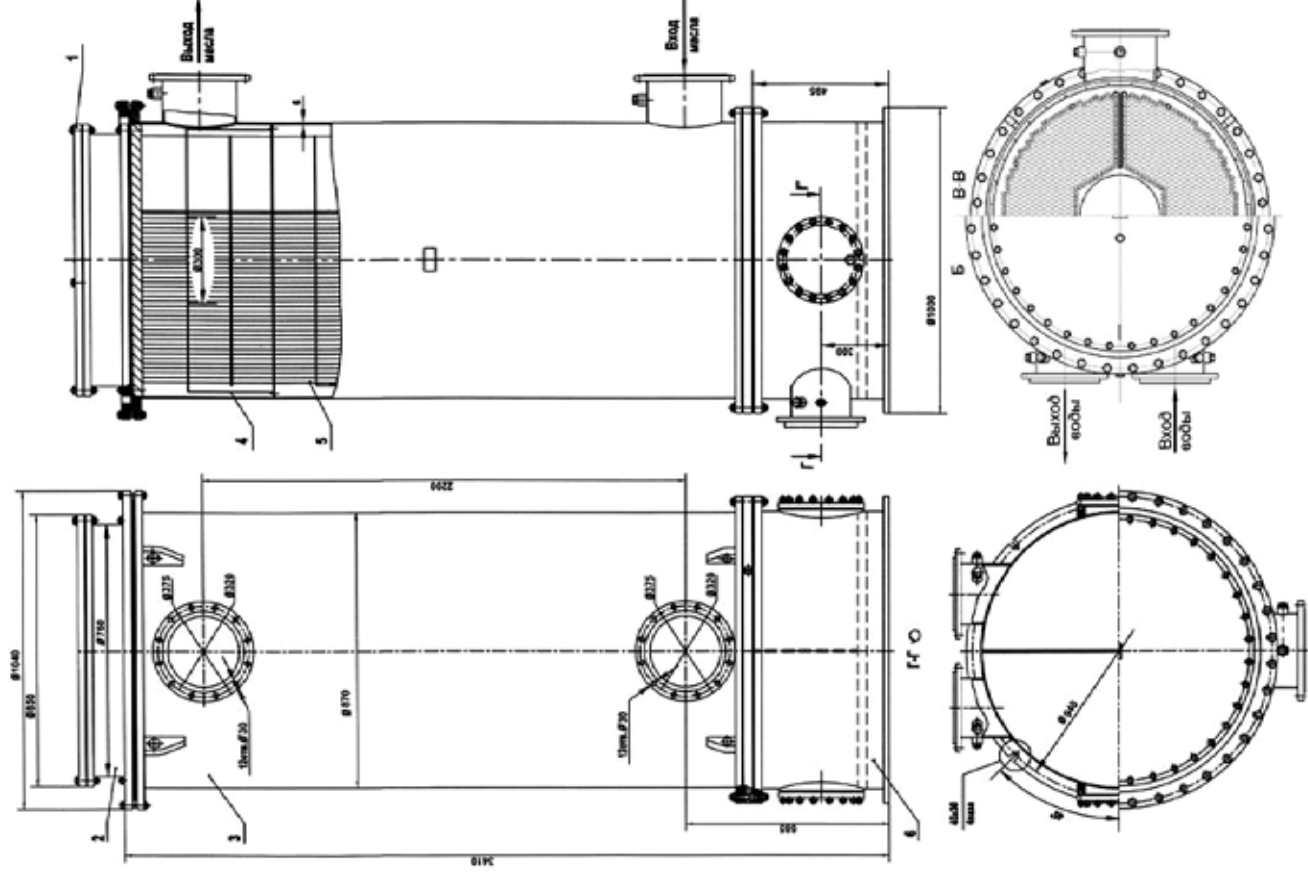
Маслоохладитель МБ-125-165: 1 – крышка; 2 – верхняя водяная камера; 3 – корпус; 4 – кожух; 5 – трубная система; б – нижняя водяная камера
